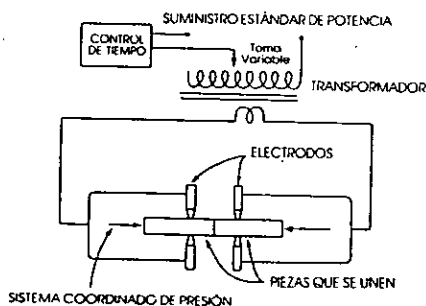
CIRCUITO DE SOLDADURA POR RESISTENCIA
